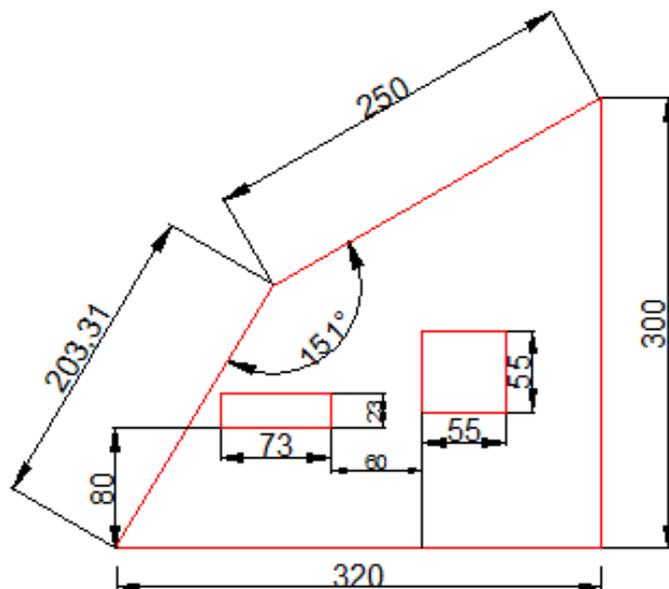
2 Diseño de la vista lateral derecha. Diseño en AutoCAD de la vista frontal del módulo PLC
